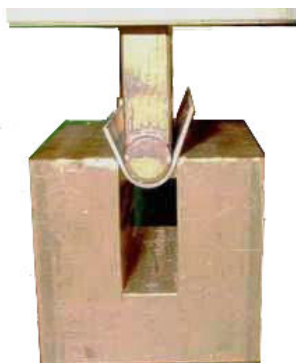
Mechanisches Presswerkzeug zur Durchführung von Biegeversuchen
